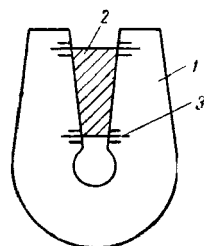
Шаблон для проверки профиля коллекторных пластин:
